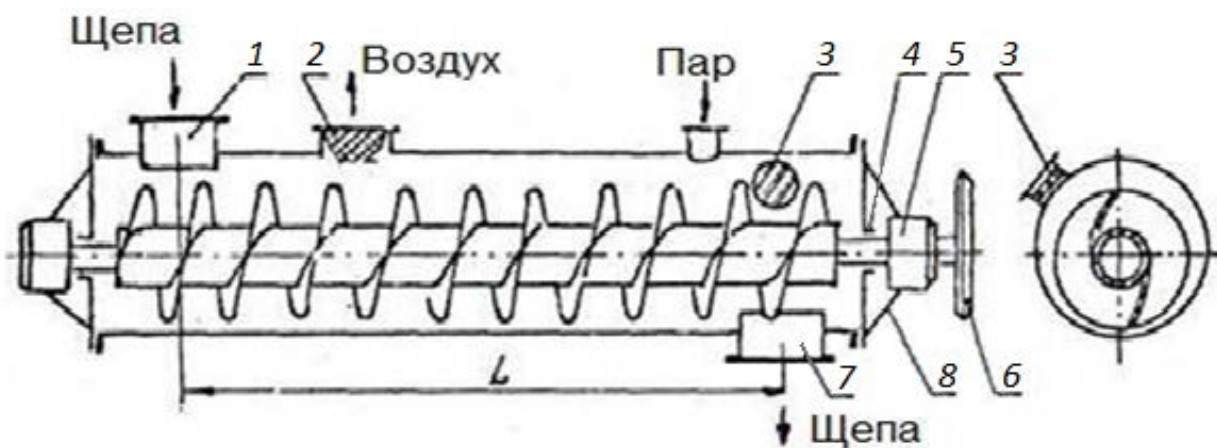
Пропарочная цистерна: 1 – патрубок для подачи щепы; 2 – патрубок с сеткой; 3 – смотровое окно; 4 – сальник; 5 – подшипник; 6 – звездочка привода; 7 – патрубок для выхода щепы; 8 – укосины для крепления подшипников
